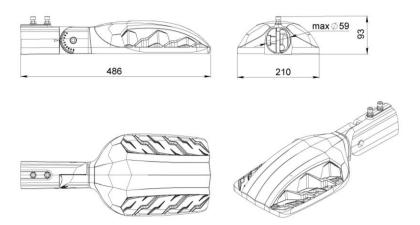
Общий вид светильника Street X1 с консольным поворотным креплением.
